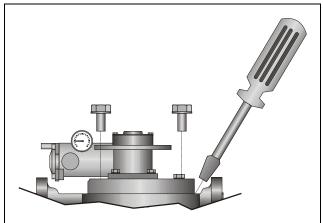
Desserrer les vis hexagonales sur le couvercle du filtre
